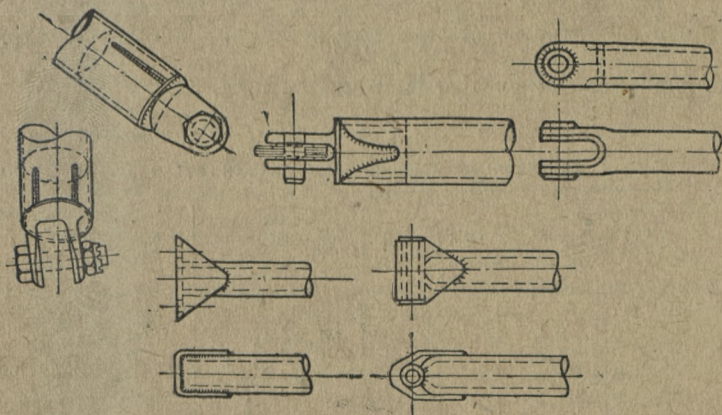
Примеры замены оторванного уха при помощи сварки
